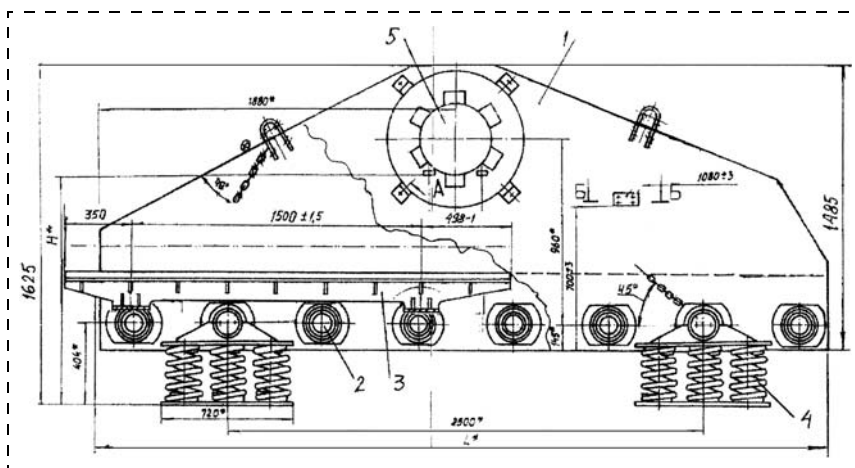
Модернизированный грохот ГИТ-51М для разделения известняка и глинистых включений: 1 — рабочий орган, включающий связь-балки 2 и колосниковую просеивающую поверхность 3; 4 — упругие опоры; 5 — дебалансный привод
